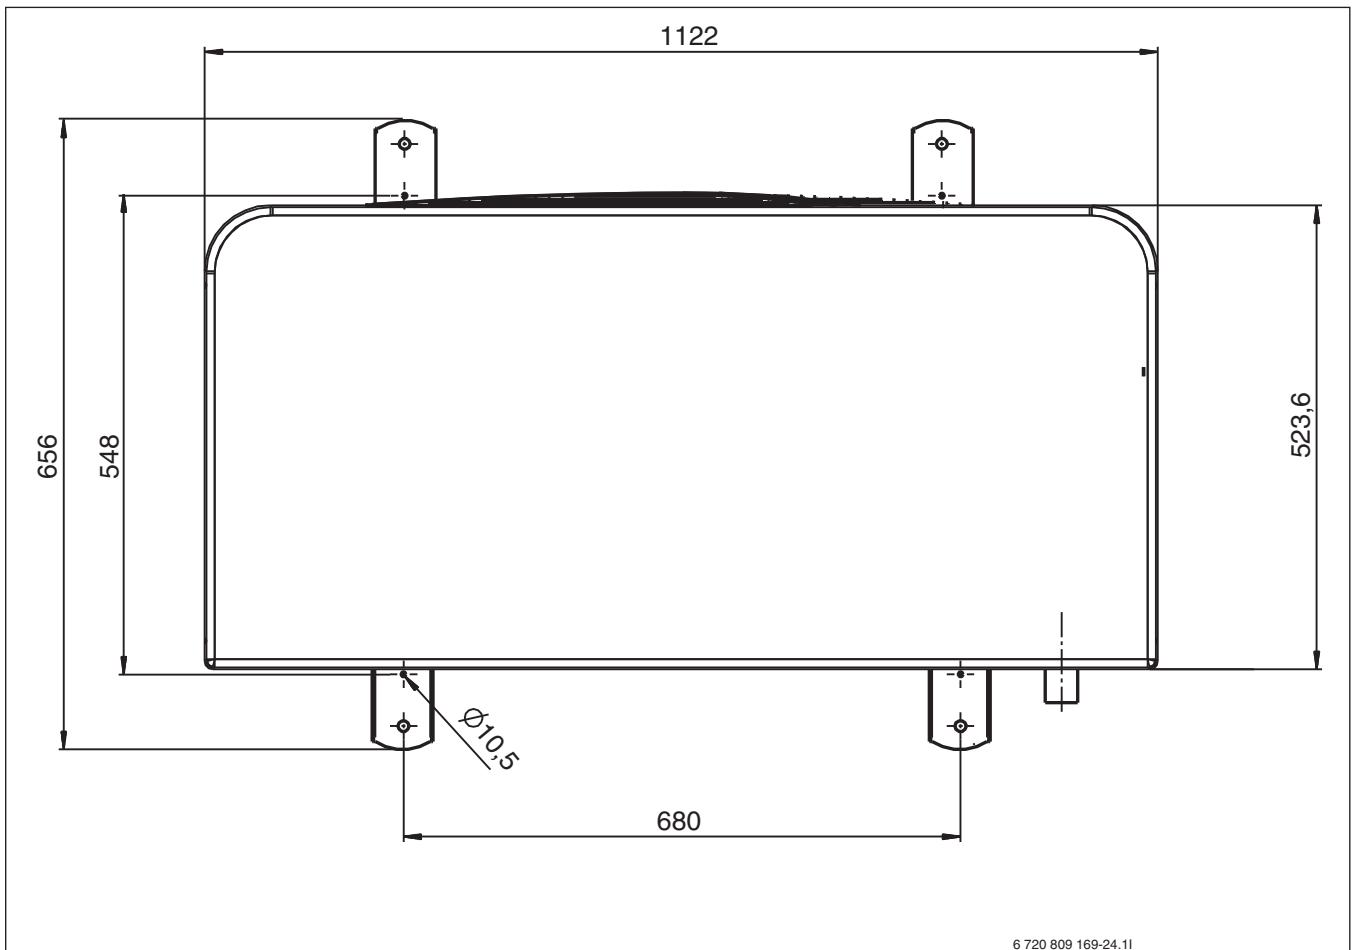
Dimenzije Compress 6000 AW 5,7 in 9, pogled od zgoraj
